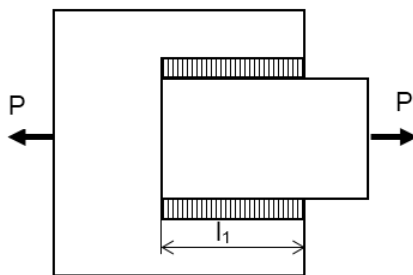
До розрахунку флангового внапуск зварного шва
